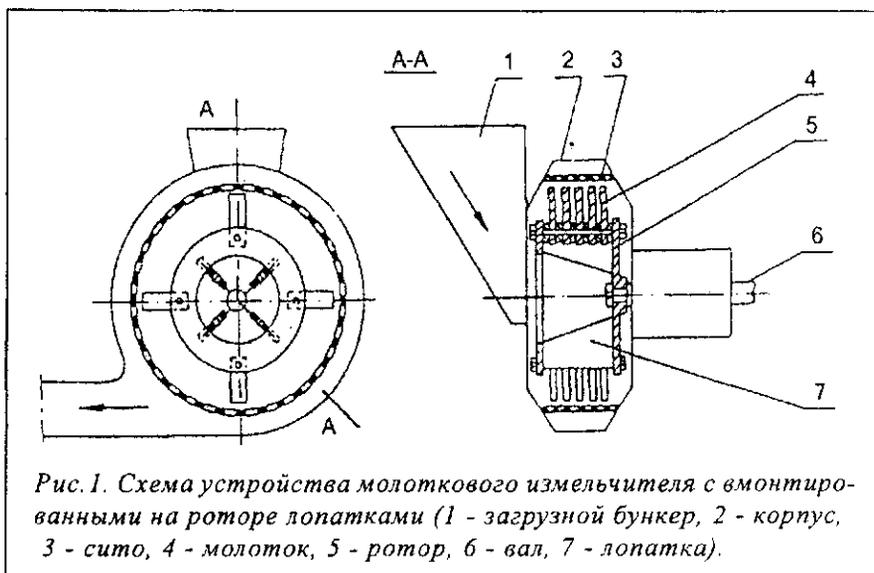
Схема устройства молоткового измельчителя с вмонтированными на роторе лопатками (1 - загрузной бункер, 2 - корпус, 3 - сито, 4 - молоток, 5 - ротор, 6 - вал, 7 - лопатка).
